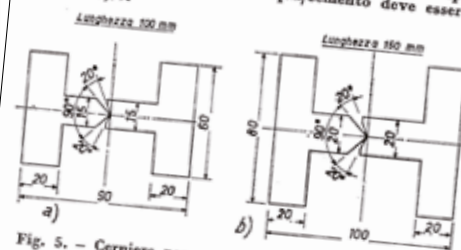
Cerniere per provetta: a) tipo A - b) tipo B.
